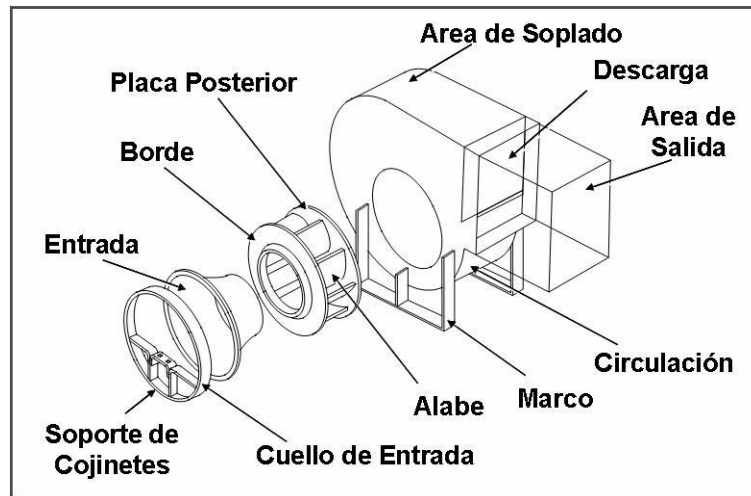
ELEMENTOS DE UN VENTILADOR
